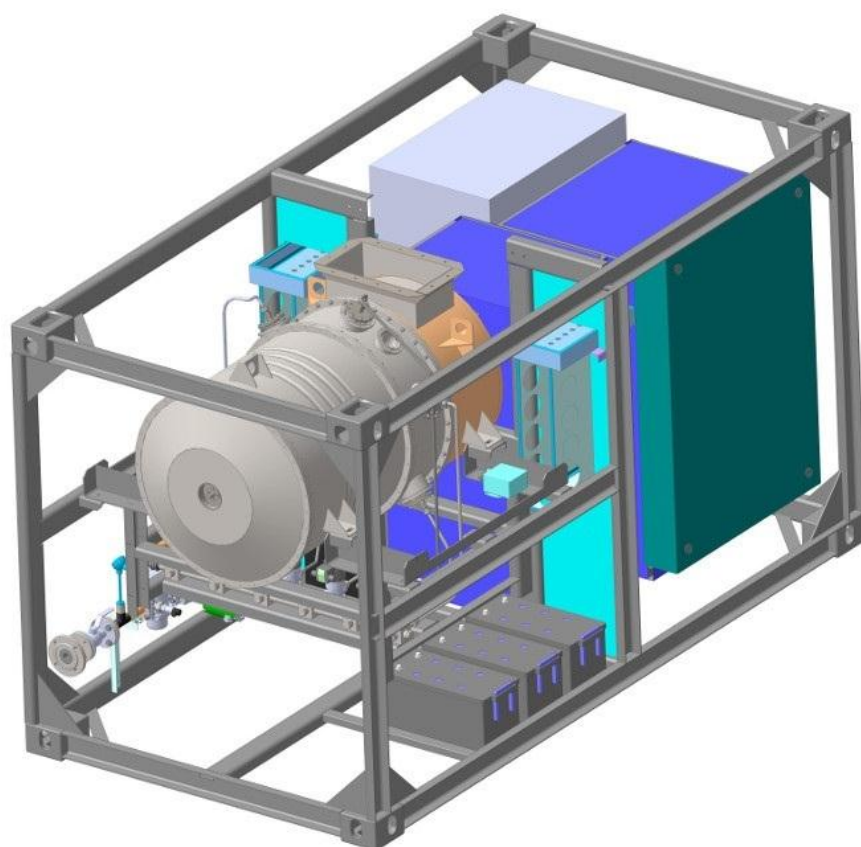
Малогабаритный газотурбинный двигатель
